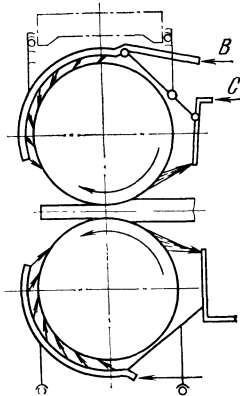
Схема конструкции для охлаждения валков и подачи смазки на сортопрокатных станах:
